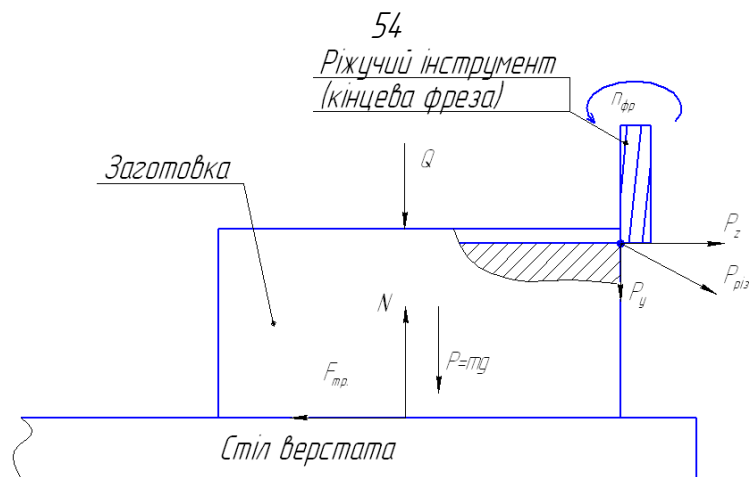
Схема сил, що діють на заготовку в процесі обробки
